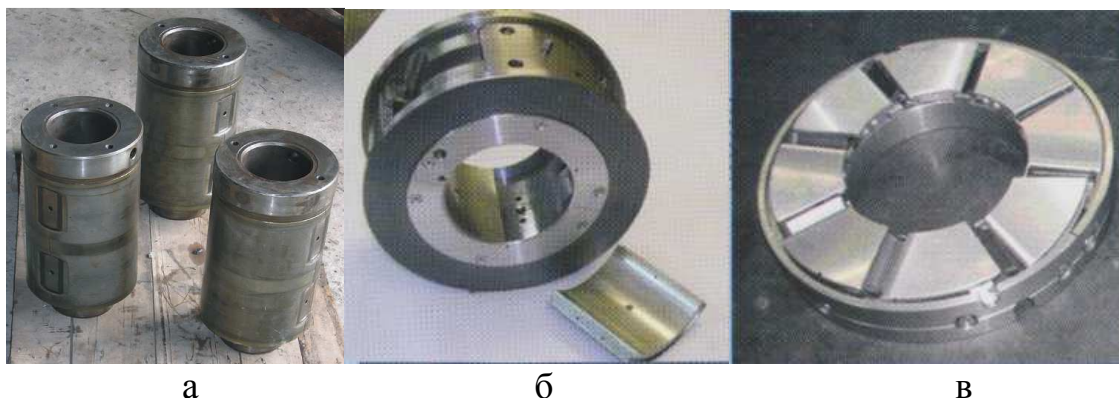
Конструктивні елементи ПК з бабітовим покриттям: а – зовнішня поверхня опорних пальців зубчатих коліс, б – внутрішня поверхня вкладишів опорних ПК, в – плоска поверхня упорного ПК.
